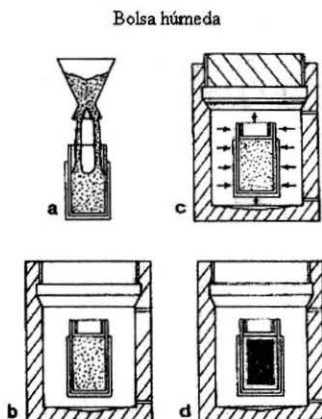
Etapas durante el prensado isostático. (a) llenado, (b) carga, (c) prensado y (d) descompresión, previa a remover la pieza compactada.
